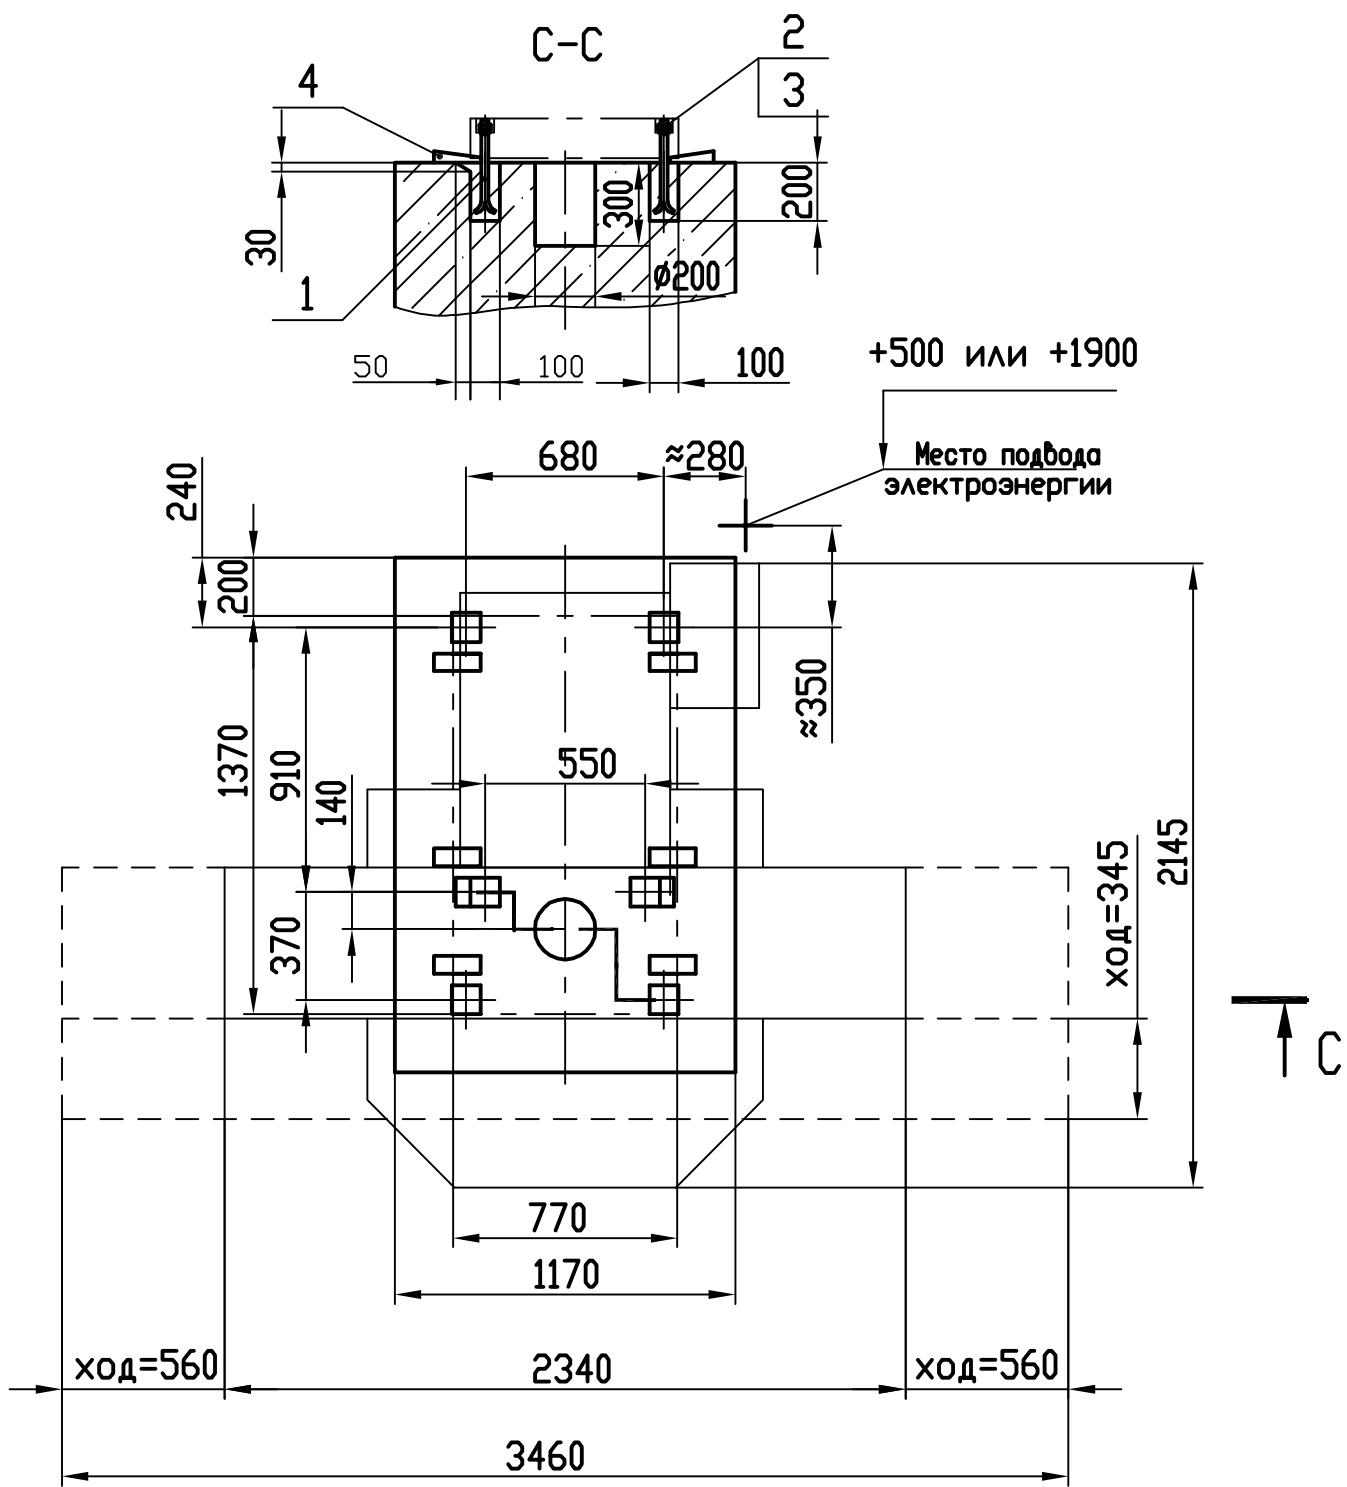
Монтажный чертеж для станков FU/FW450MRApUG
